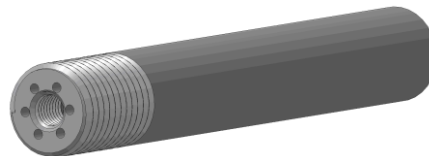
3D модель специальной сварочной горелки
